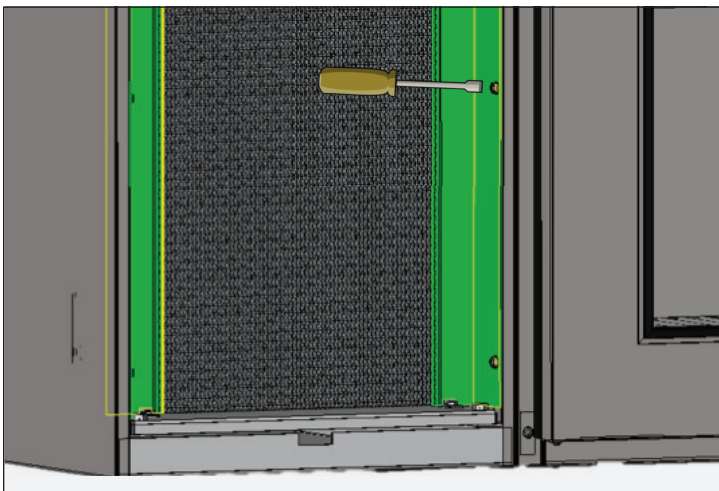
Halterungen der Verflüssigerrohre entfernen
